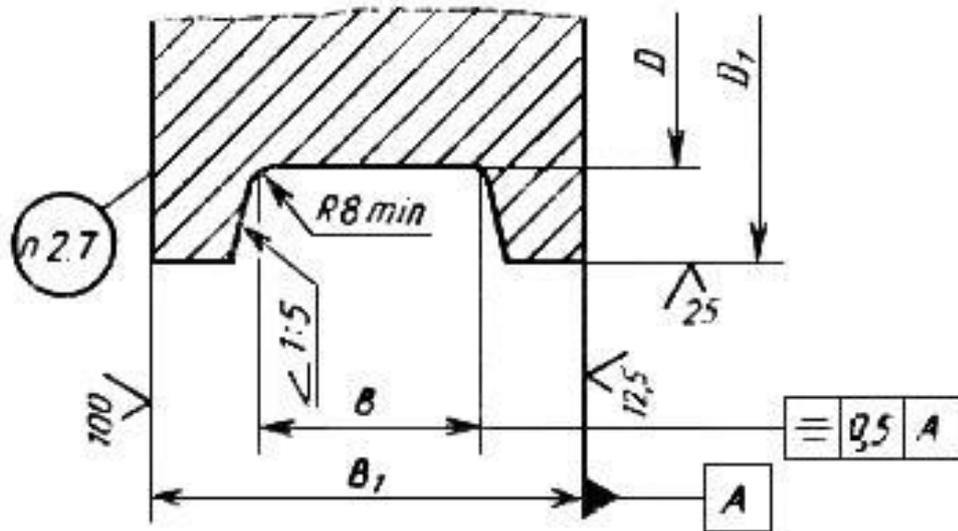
Профиль обода колеса типа К2Р по ГОСТ 28648-90
